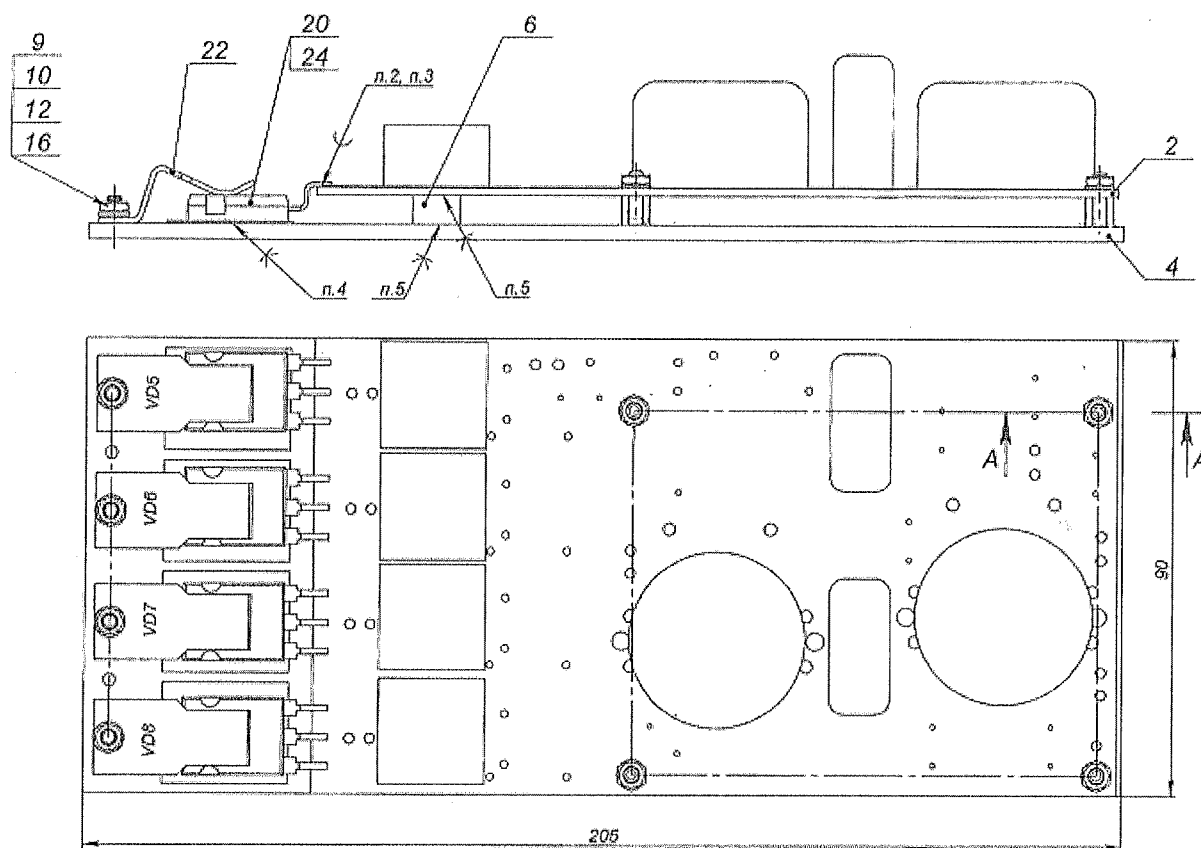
Сборочный чертеж фильтра АГБР.240.50.00.00
